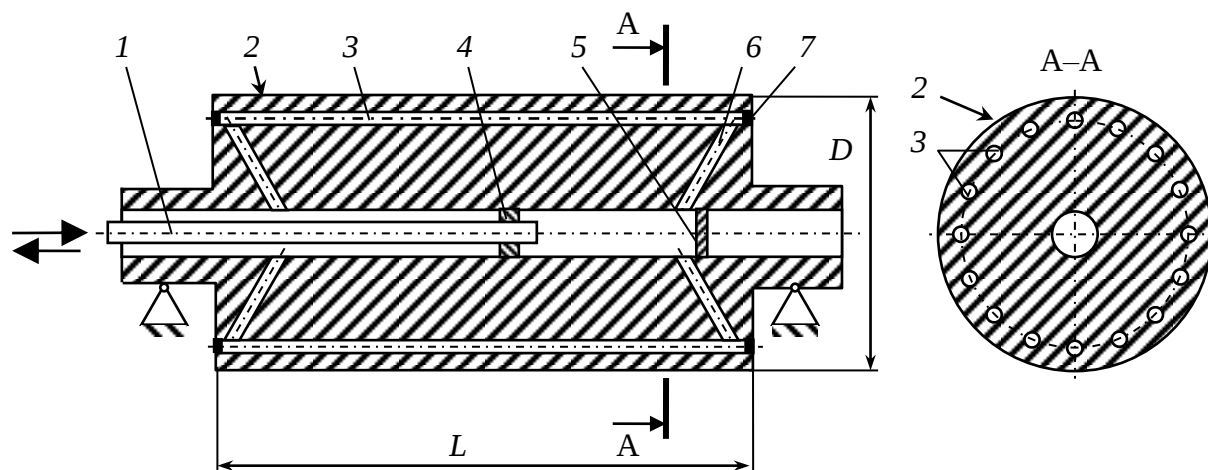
Схема валка з периферійними каналами: 1 – труба для подавання теплоносія; 2 – робоча поверхня бочки валка; 3 – периферійний канал; 4 – поршень; 5 – заглушка; 6 – похилий канал; 7 – пробка периферійного каналу
